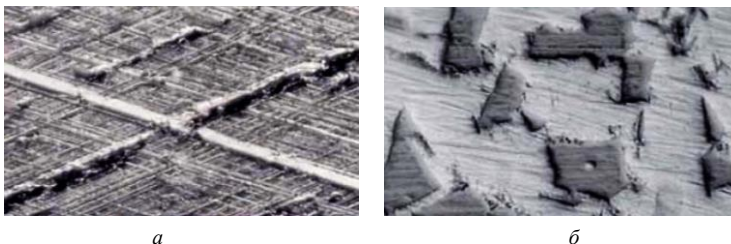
Внешний вид рабочей поверхности чугунных (а) и алюминиевых (б) цилиндров
